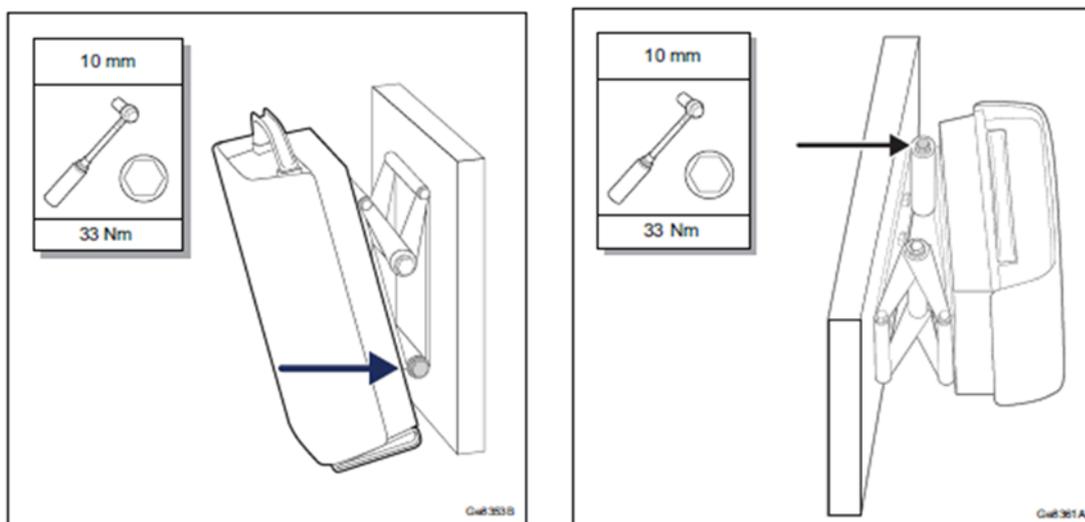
MONTAJE DE UNIDAD REMOTA DE RADIO
